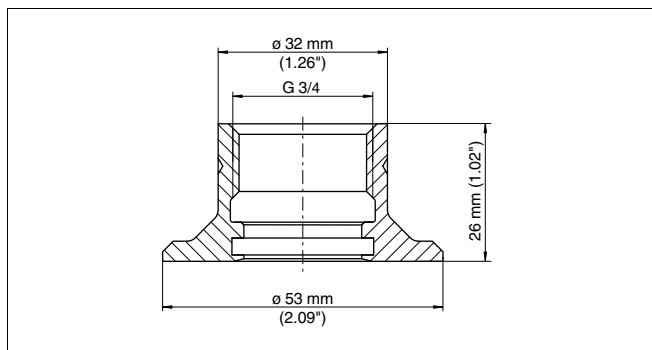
Medidas da luva soldada G $\frac{3}{4}$ A conforme DIN 3852-X
